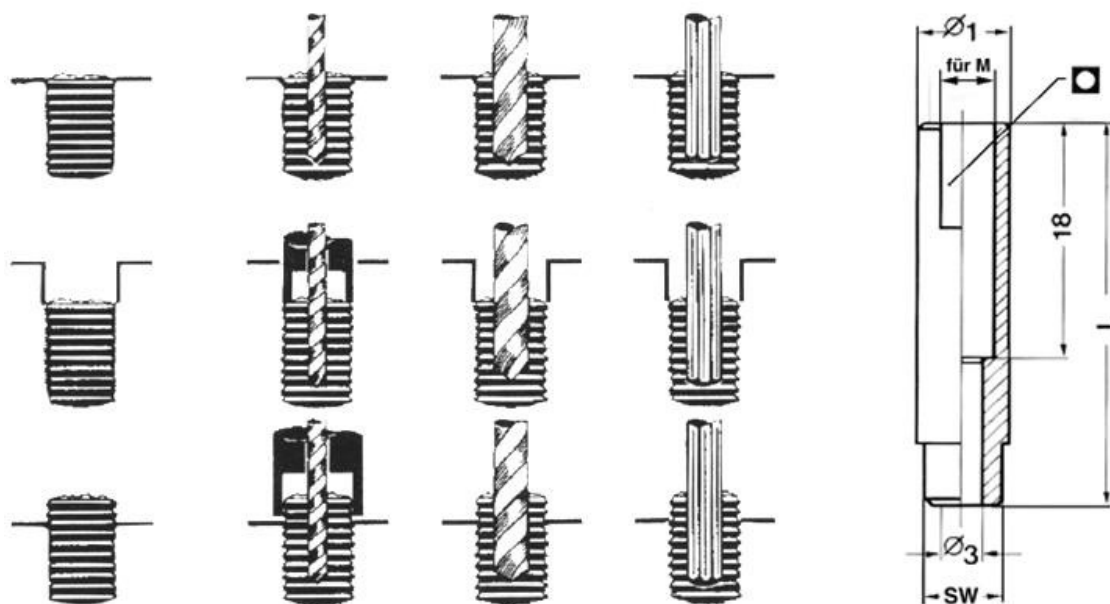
Macho para extracción del tornillo. [Q-13]
